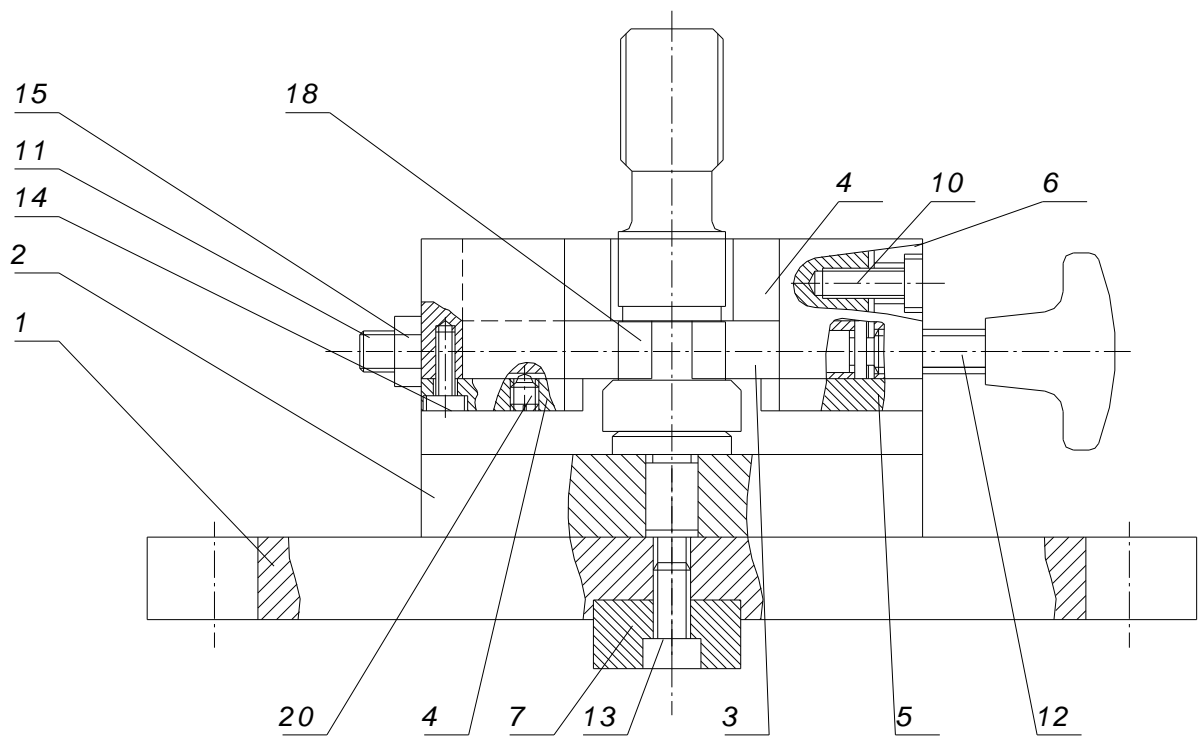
Загальний вид пристосування для фрезерування пазу.
